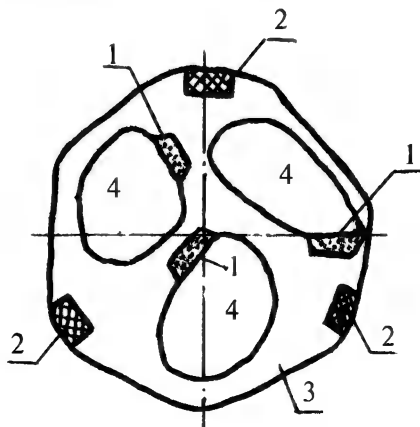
Многорезцовая сверлильная головка: 1- резец, 2 - направляющие, 3 - корпус, 4 - полость для отвода стружки
